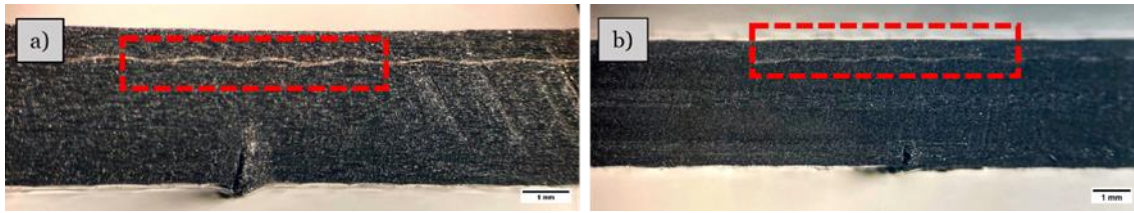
Análise do estado do defeito depois do teste mecânico. a) construção unidirecional e b) construção cruzada.
